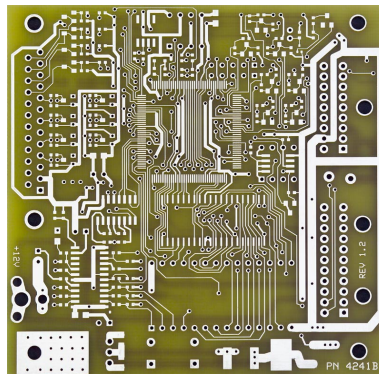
Ejemplo de prototipo inicial PCB.
